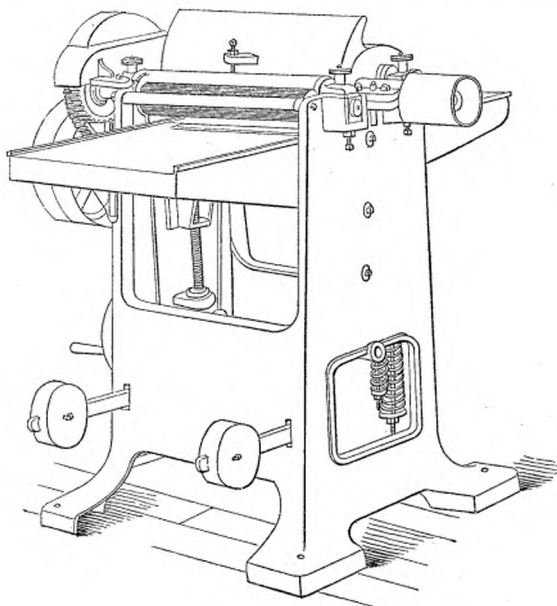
Machine à raboter n° 1 de la Egan Company.
